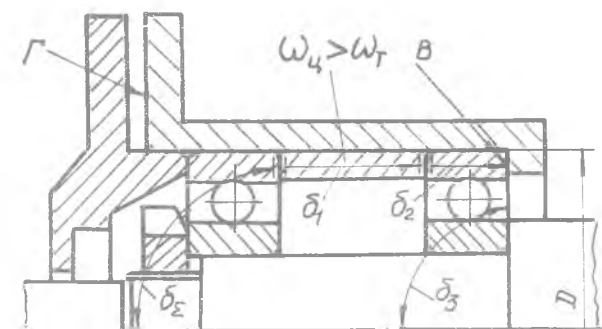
Установка промежуточного кольца между наружными кольцами подшипников
